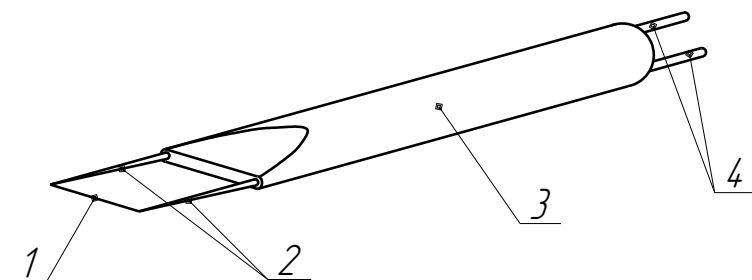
Схема чутливого елемента із дроту: 1 – нитка, що нагрівається; 2 – підтримуючі ніжки; 3 – корпус; 4 – виводи
